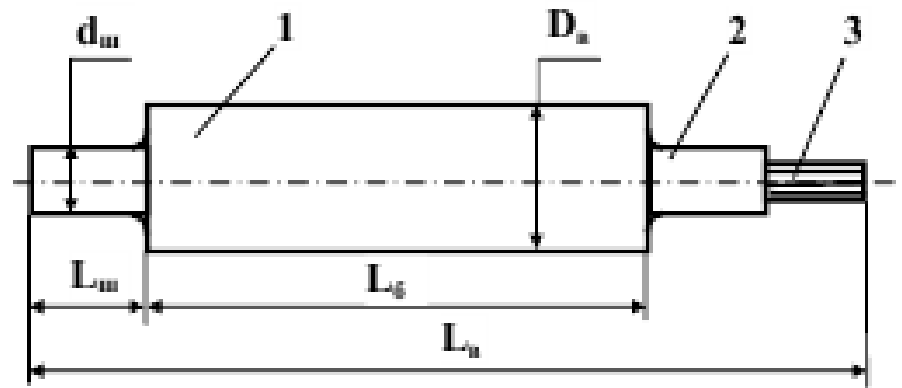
Прокатний валок: 1 – бочка прокатного валка; 2 – шийка прокатного валка; 3 – хвостовик прокатного валка; $D_б$ – діаметр бочки прокатного валка; $d_ш$ – діаметр шийки прокатного валку; $L_ш$ – довжина шийки прокатного валку; $L_б$ – довжина бочки прокатного валку
